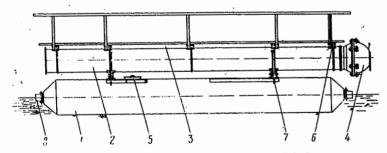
Поплавок к земснаряду типа 500-60. 1 — понтон; 2 — труба; 3 — настил; 4 — шаровое соединение; 5 — люк; 6 — опора для настила; 7 — ложе для труб; 8 — привальный брус.
